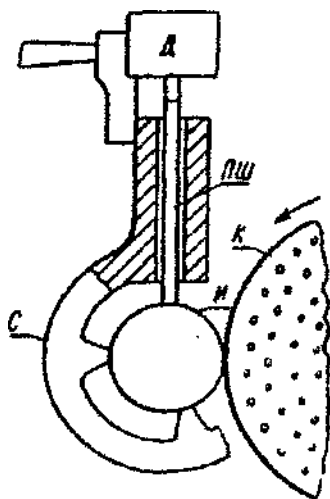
Электроизмерительная скоба для контроля диаметра обрабатываемого цилиндра:
